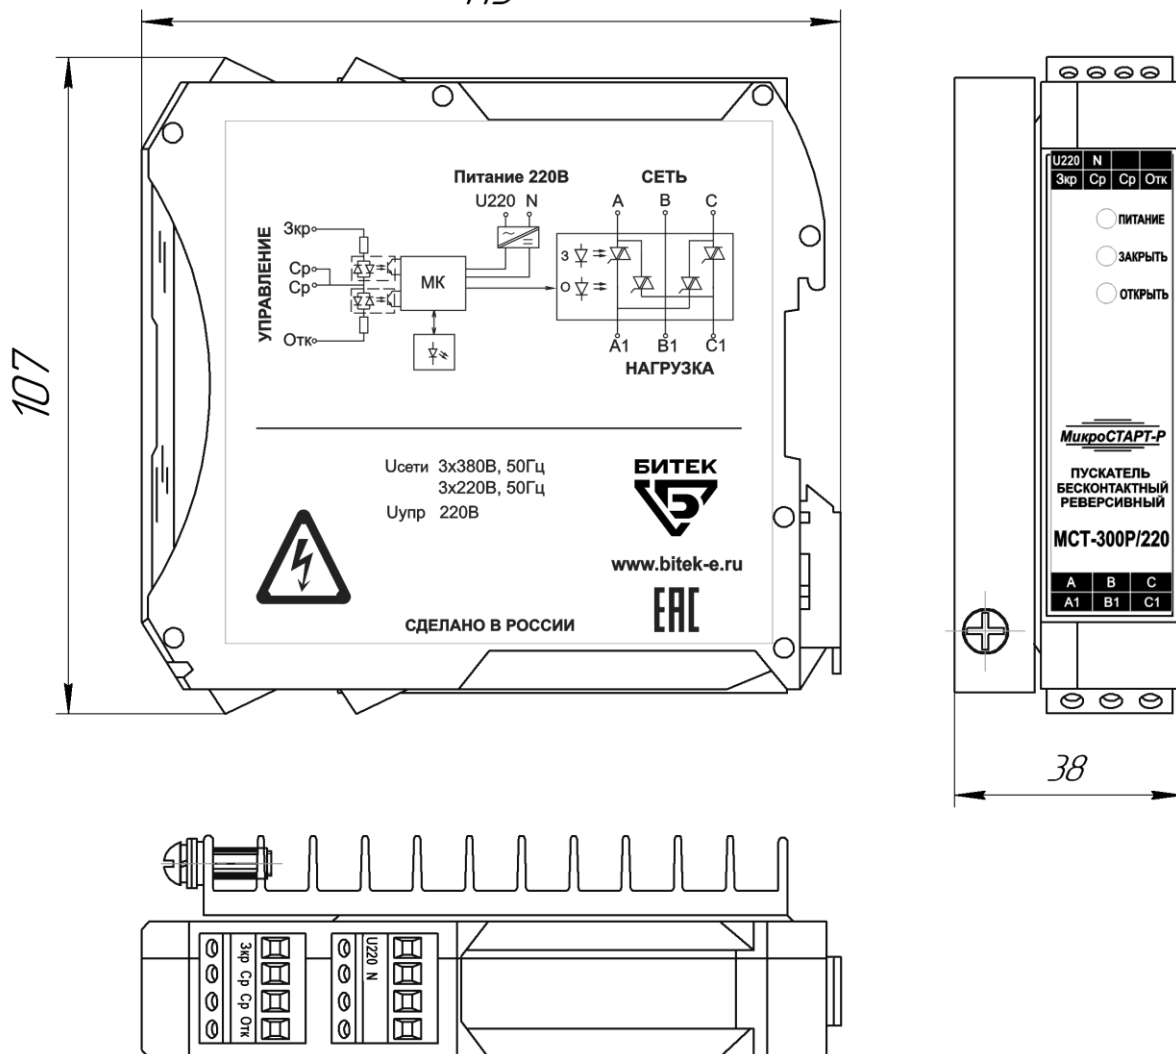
Габаритно-установочные размеры МСТ-300P/220
